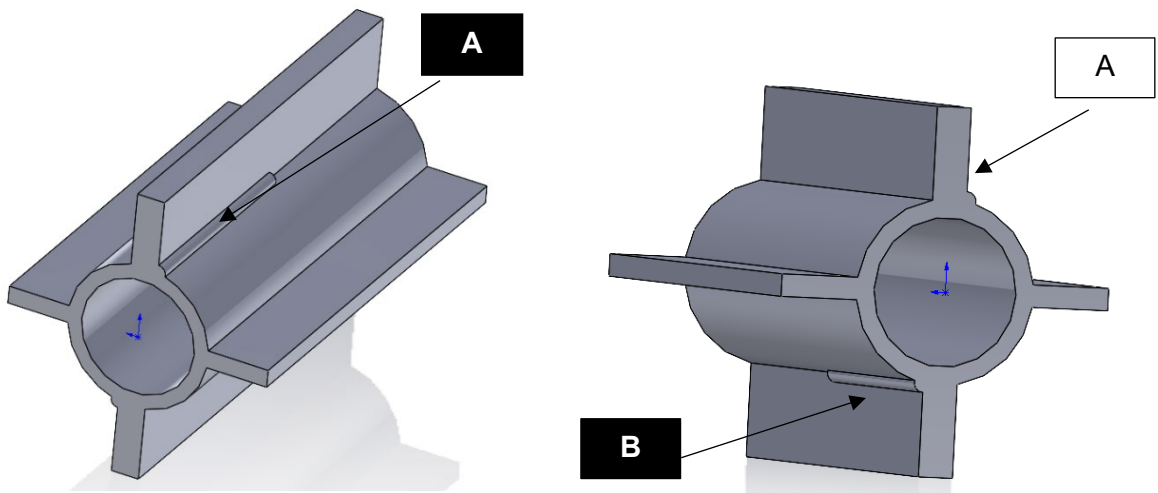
Detalle las uniones soldadas entre tubo y venas (también llamado nervios).
